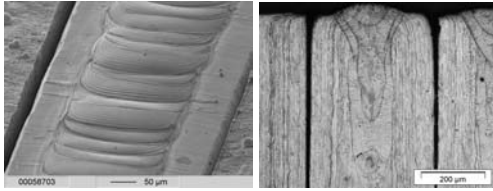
Aufsicht und Querschnitt einer Schweißnaht im Reaktorstapel (X2CrNiMo18-14-3)
